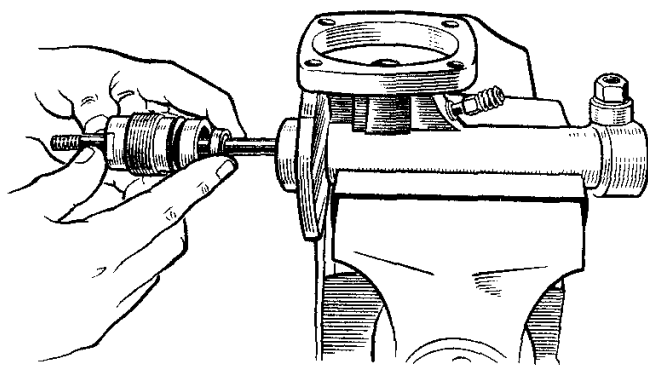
Установка вторичной манжеты в корпус уплотнителей
